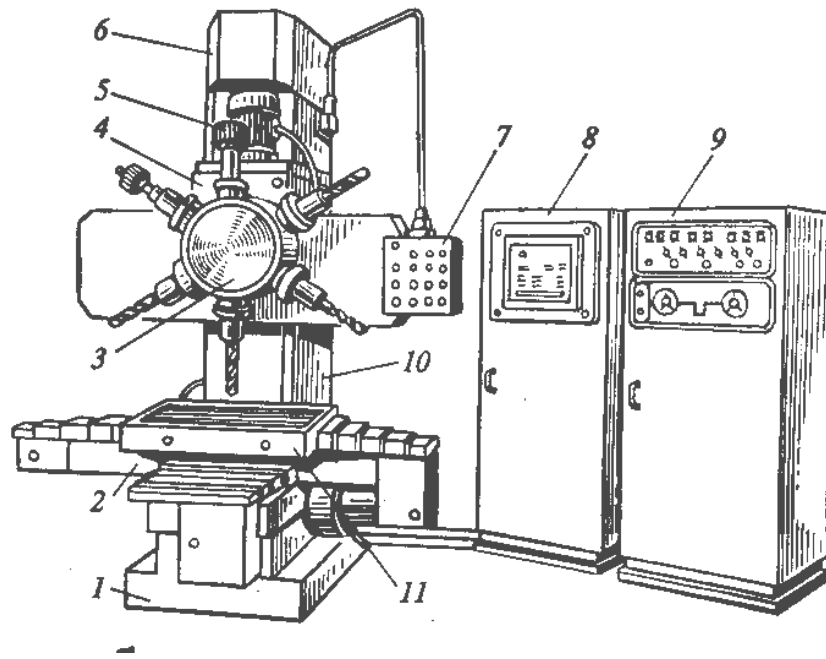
Вертикально-свердильний верстат з ЧПК з револьверною
